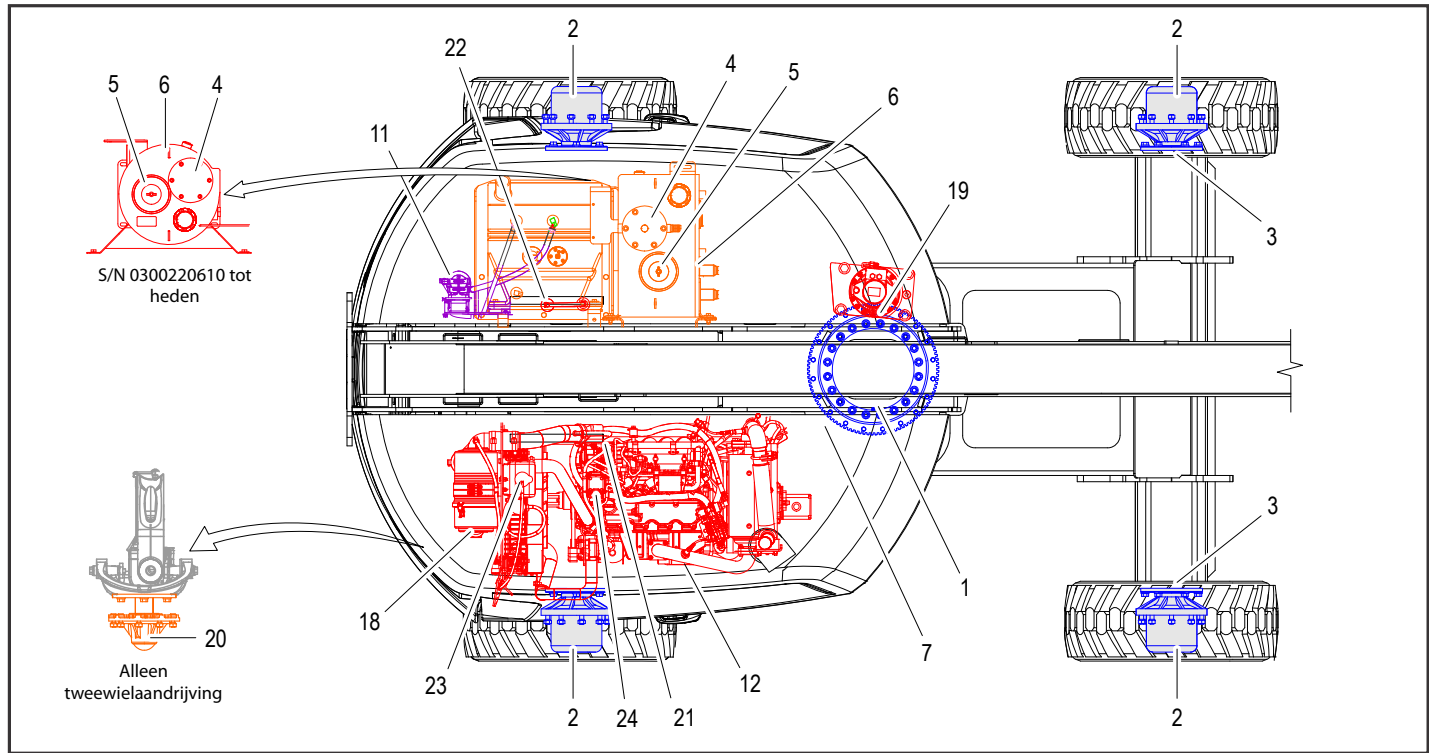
Schema voor smering en onderhoud door machinist – Deutz 2011L-motor
